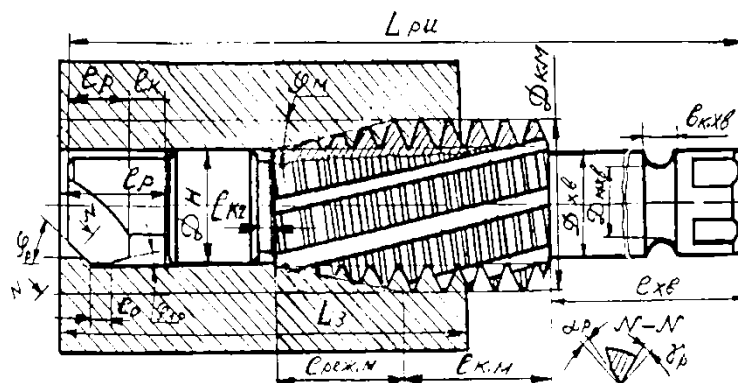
Схема нарезания резьбы комбинированным инструментом «Расточной резец-метчик с направляющей»
